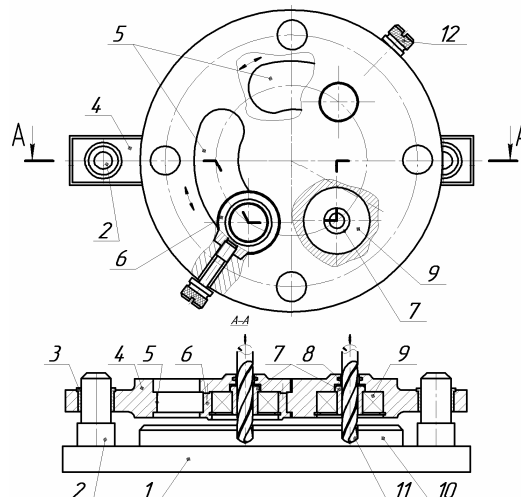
Переналаджуваний кондуктор до багатошпіндельної свердлильної головки:
